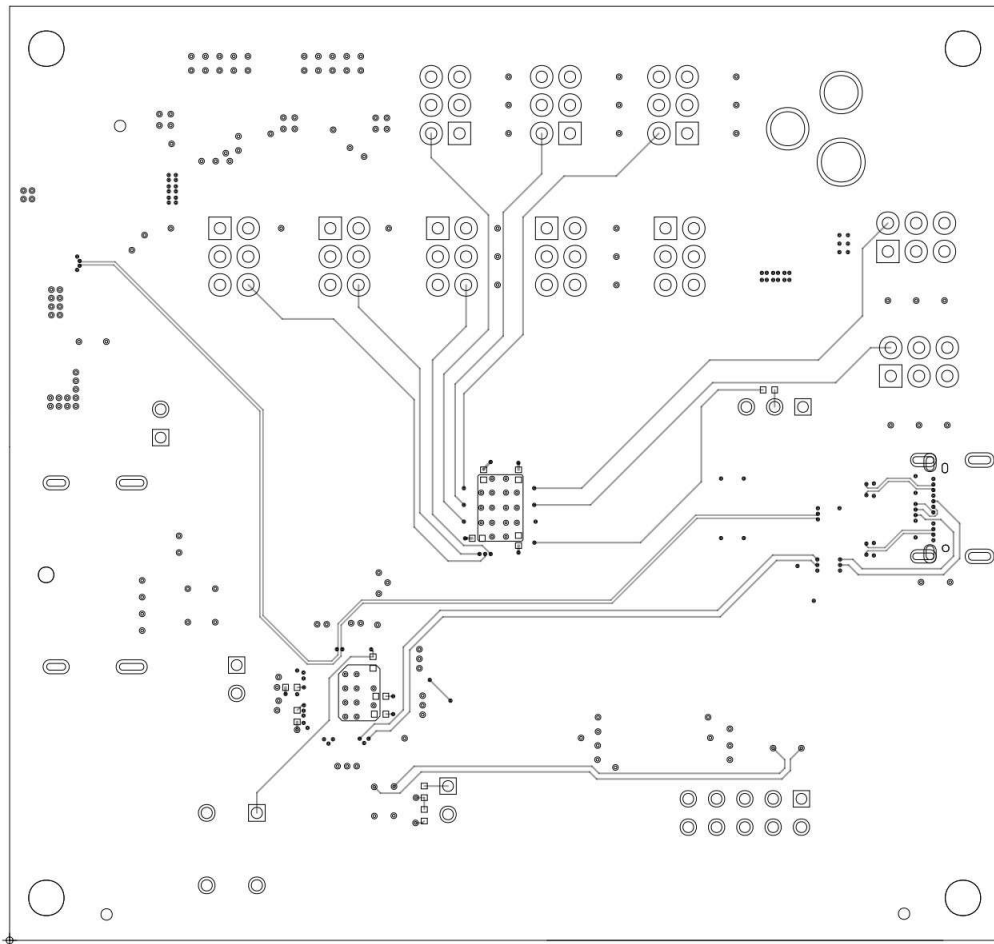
TUSB5461-Q1 EVM PCB 第 6 层 (底部)
